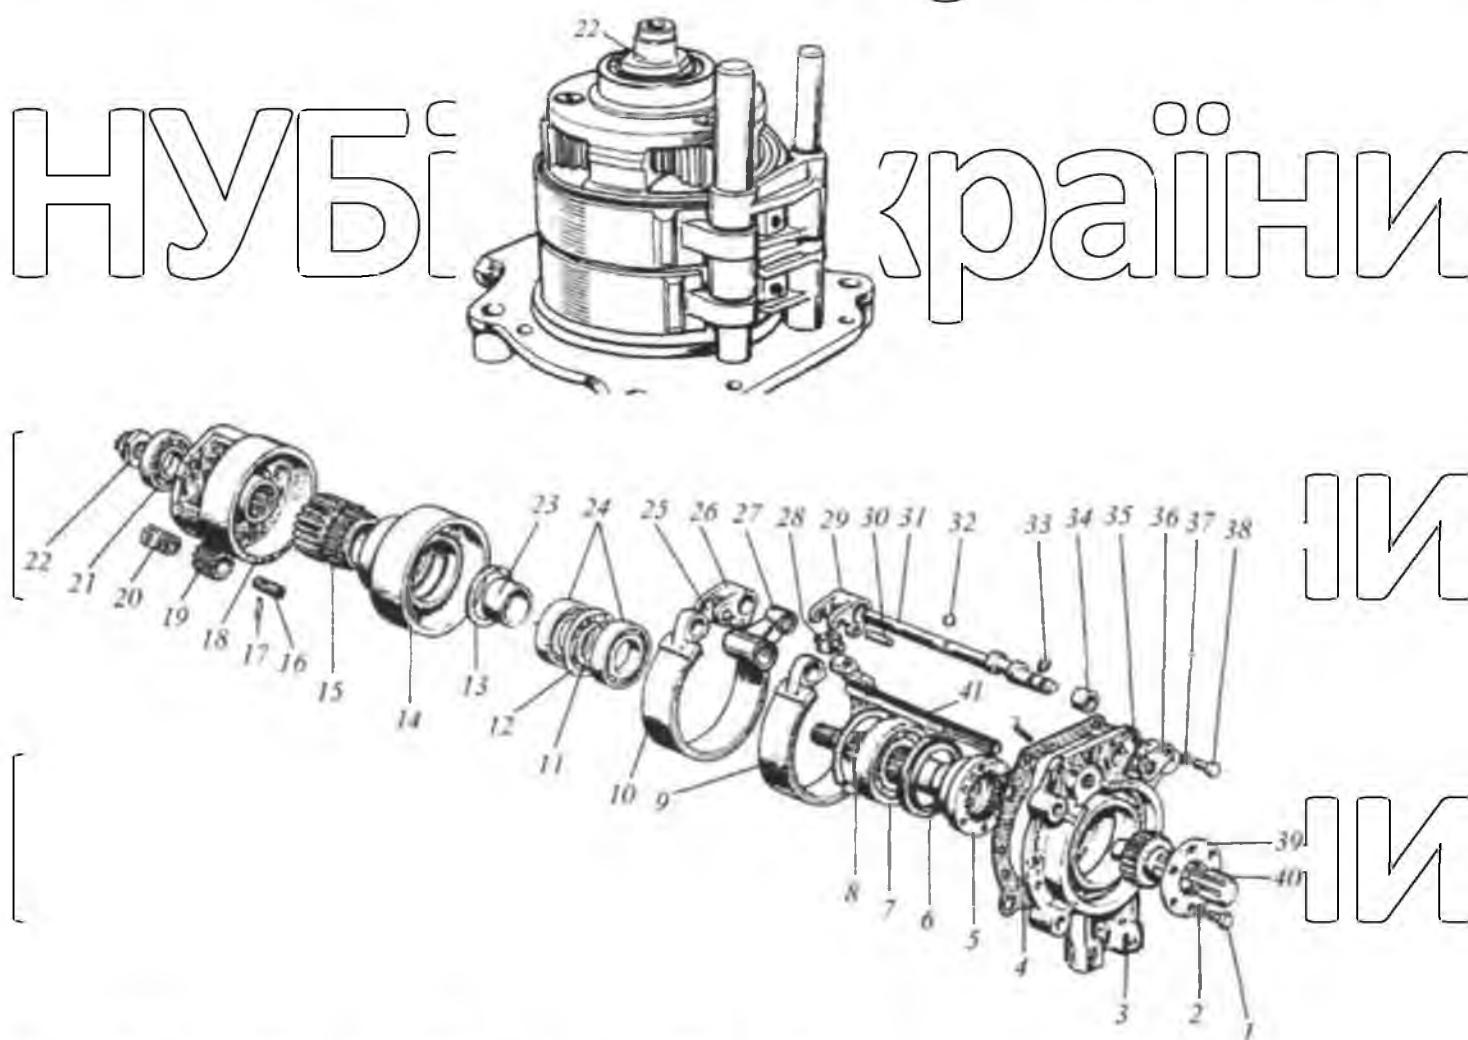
Планетарний редуктор ВВП: 1, 38 - болт; 2, 37 - шайби; 3 - кришка; 4 - прокладка; 5 - вал; 6 - манжета; 7 - підшипник; 11, 12, 13 - стопорне кільце; 9, 10 - стрічки; 14 - барабан; 15 - шестерня сонячна; 16 - вісь сателіта; 17, 30 - штифт; 18 - водило; 19 - сателіт; 20 - підшипник; 21, 24 - шарикопідшипник; 22 - гайка; 23, 34 - втулка; 25, 28 палець; 26, 29 - важіль; 27 - кронштейн; 31 - ексцентрикова вісь; 32, 33, 35 - кільце; 36, 39 - пластини; 40 - хвостовик змінний (8, 6 або 21 шліц); 41 - вісь.
